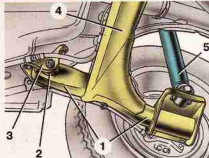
Подвеска правого заднего колеса: 1 — рычаг подвески; 2 — резинометаллический шарнир; 3 — кронштейн крепления рычага подвески; 4 — соединитель рычагов; 5 — амортизатор
